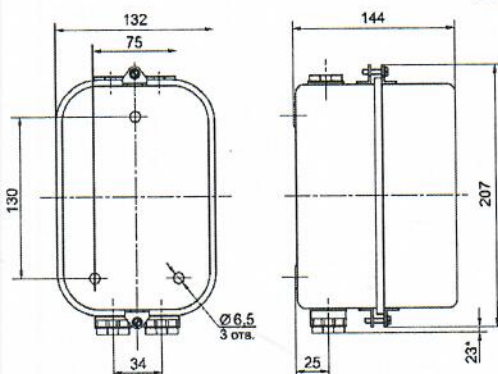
Пускатель ПМ12-025 25А в защитном корпусе. Степень защиты - IP40; IP54
